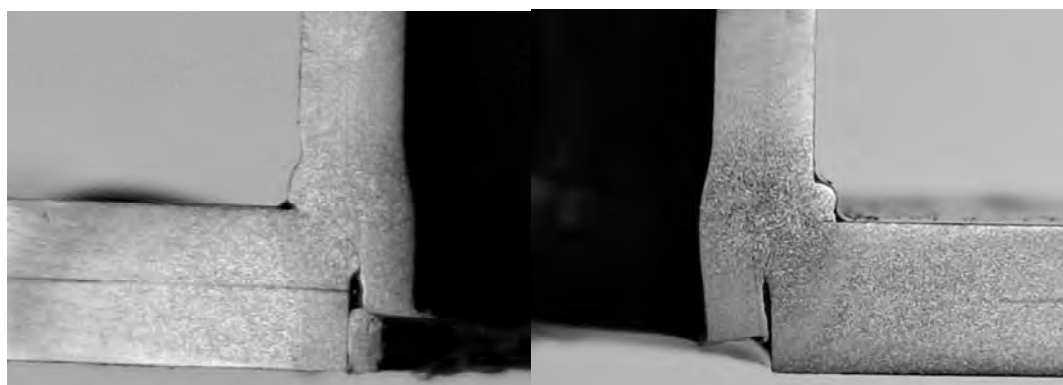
Макроструктура зоны рельефной сварки втулки с конической формой рельефа и заступом на ее торце с пластиной
